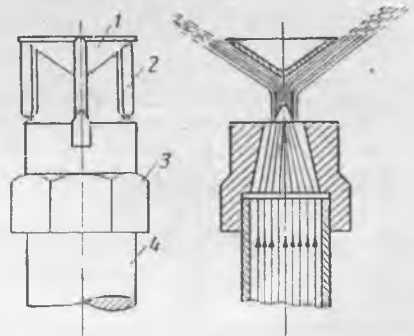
Общий вид и разрез нерегулируемой насадки:
